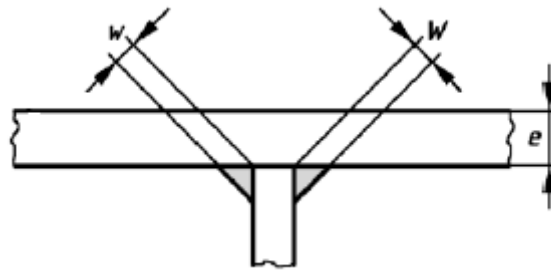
Soldadura de piezas a tope con ángulo de 90°
